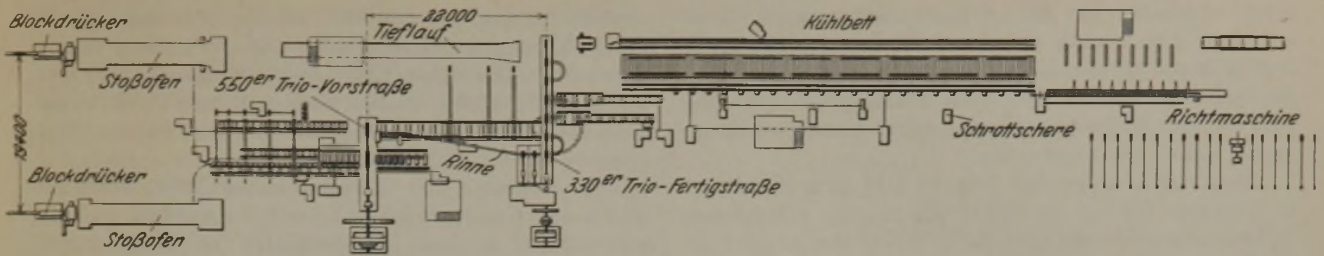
Grundriß der Feineisenstraße nach dem Umbau.
